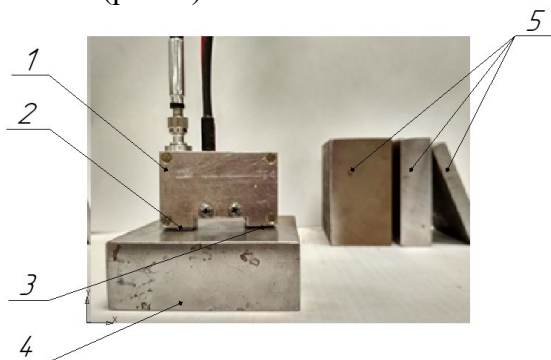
Общий вид оптико-акустического преобразователя ПЛУ-6Н-02 и образцов: 1 – корпус; 2 – призма генератора; 3 – призма приемника; 4 – образец толщиной 0,03 м; 5 – образцы толщиной 0,01, 0,02 и 0,04 м
